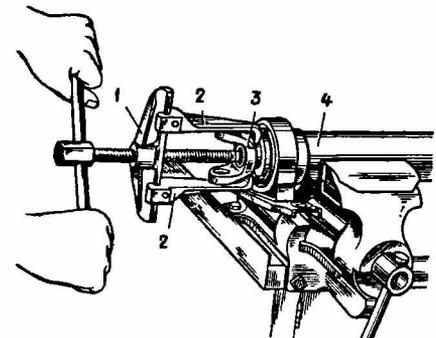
Снятие вилки с переднего карданного вала: 1 - съемник А.40005/1/5; 2 - рычаги съемника; 3 - вилка переднего карданного вала; 4 - передний карданный вал
